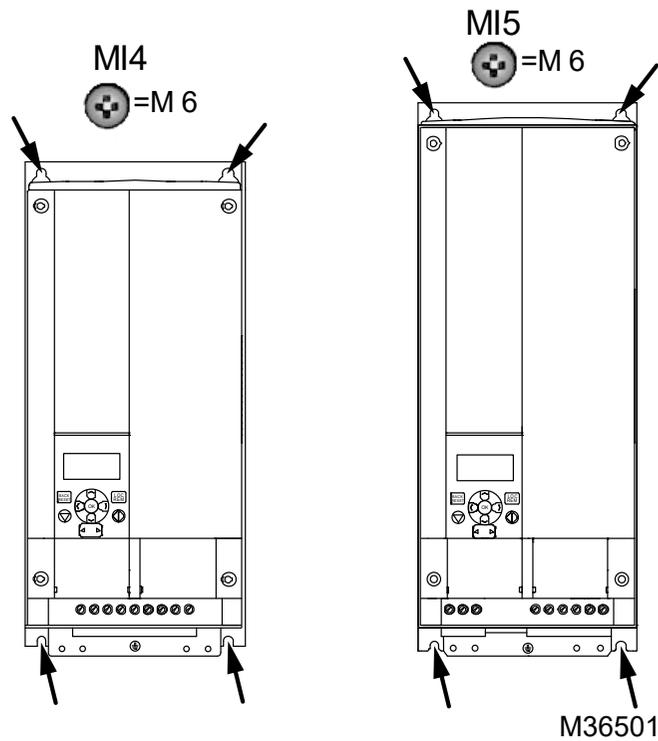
Schraubbefestigung, MI4 - MI5
